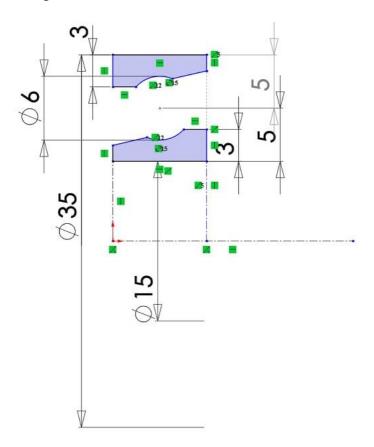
Эскиз детали 1, части 1: внешнее и внутреннее кольца подшипника
